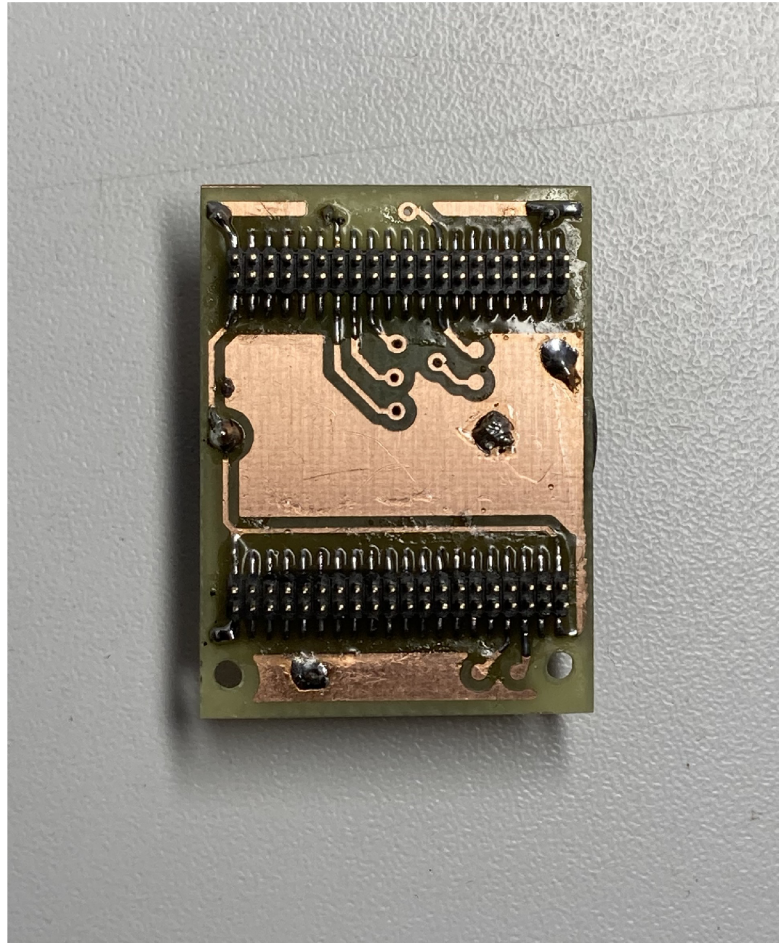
Vrchní strana desky plošných spojů pomocné desky pro měření.
